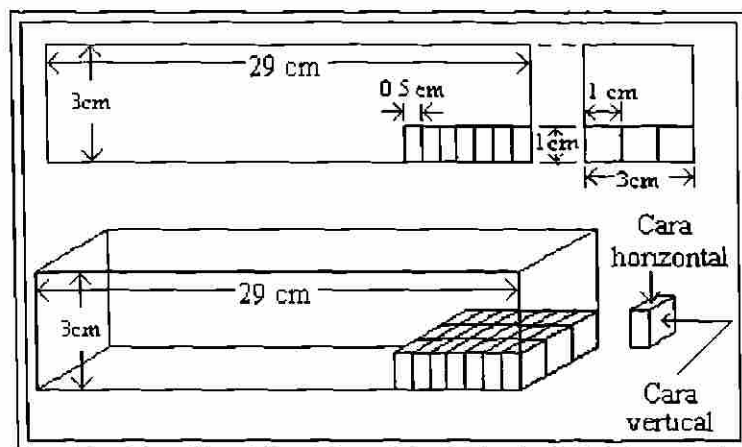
1. Molde con paredes metálicas, en un caso fondo con fondo de arena y en otro fondo metálico.
